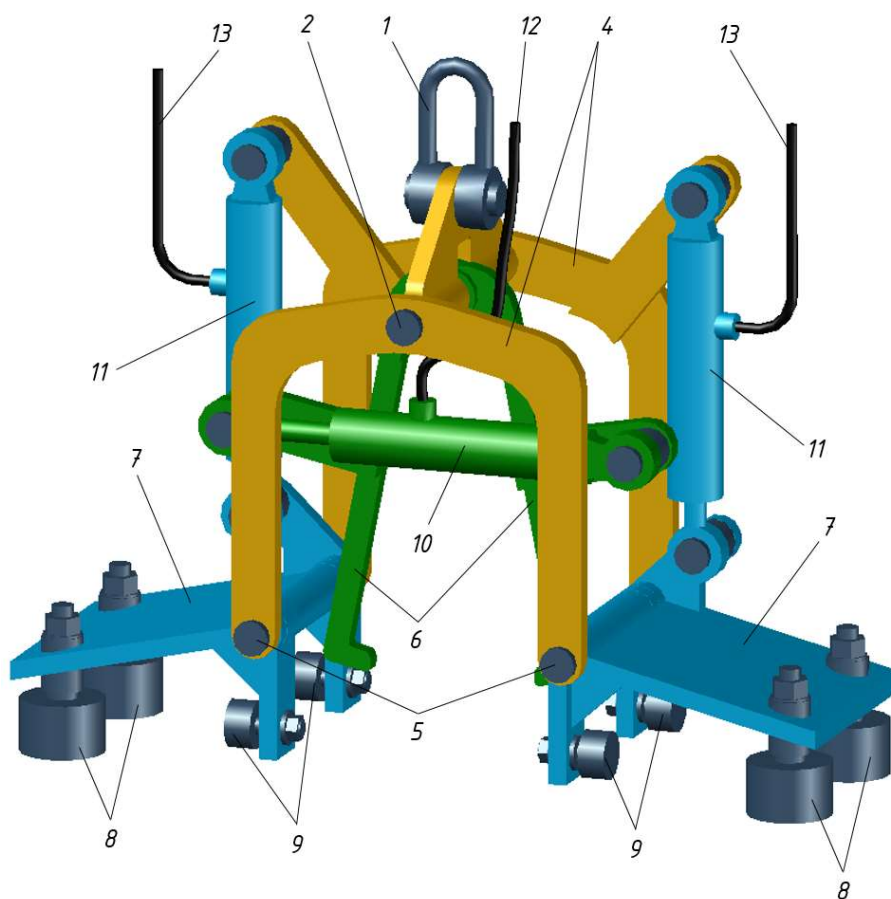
3D вид двойного роликового рельсового захвата
